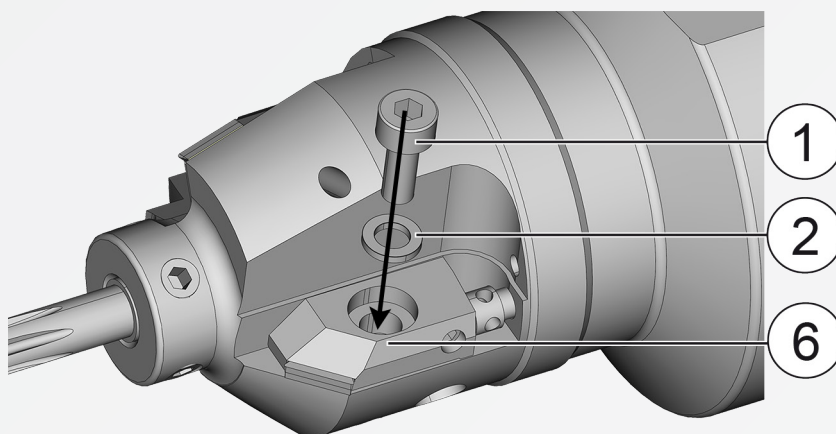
Spannpratze mit der Spannschraube und der Unterlegscheibe fixieren
